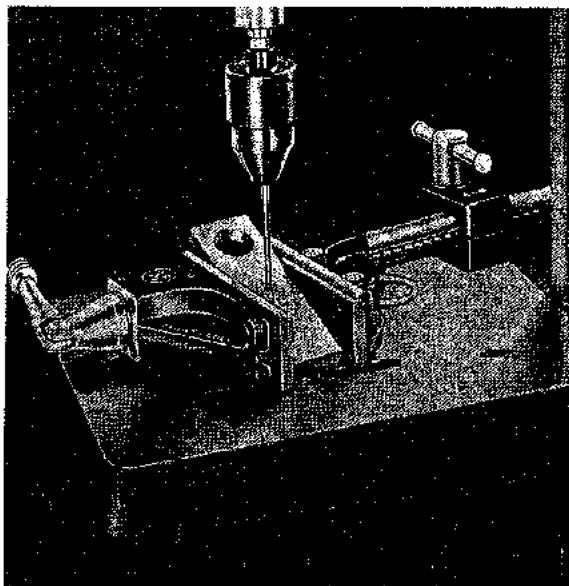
Una mordaza de seguridad para taladradora, fijada a la mesa, puede sujetar la pieza en cualquier posición (American Machine & Foundry Co.)
